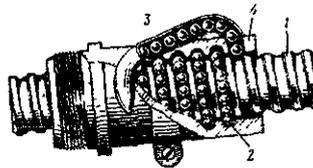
b Vista en corte de un tornillo con rodamientos.
